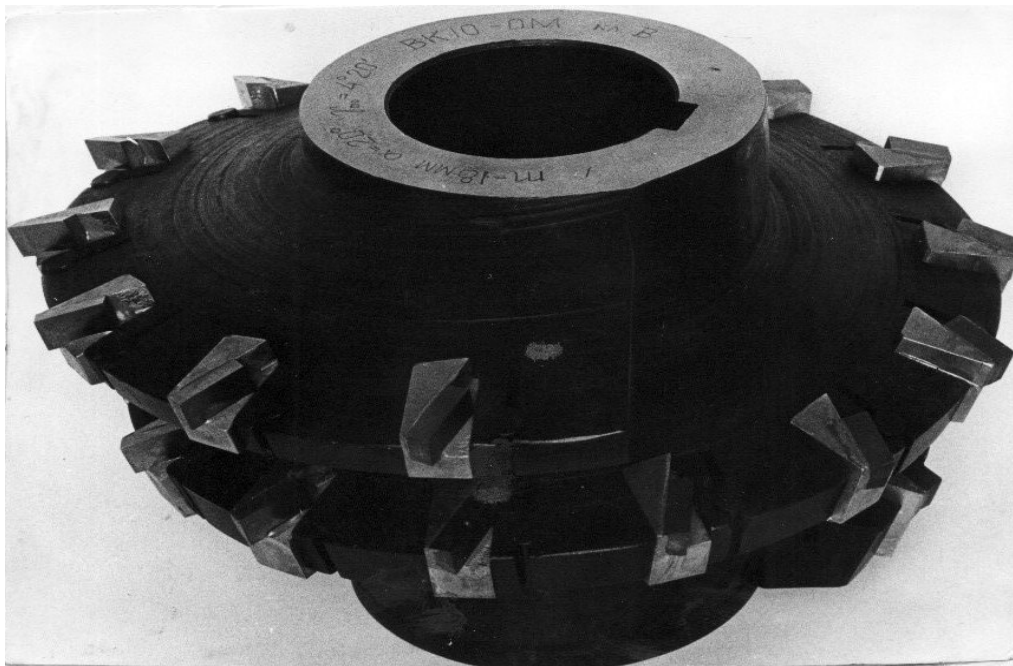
Левый корпус червячной фрезы  $m=18$  мм со вставными резцами и напаянными пластинами под углом наклона  $\lambda = -30^{\circ}$ .
